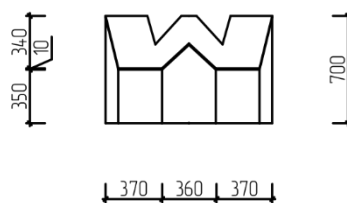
Чертеж оборудования. Вид прямо
